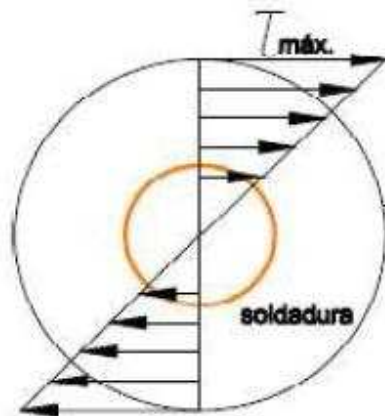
Esfuerzo cortante en la soldadura eje de rueda – piñón conductor.
